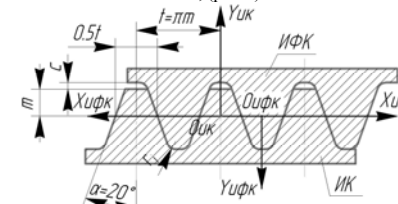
Стандартный исходный реечный контур и совпадающий исходный формообразующий реечный контур не модифицированной цилиндрической эвольвентной зубчатой передачи
